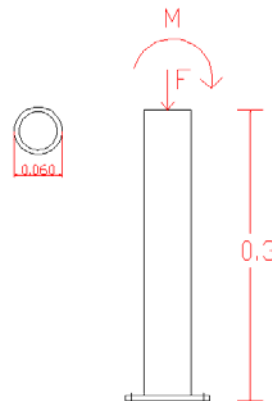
COLUMNA DE SOPORTE PARA LA OLLA
